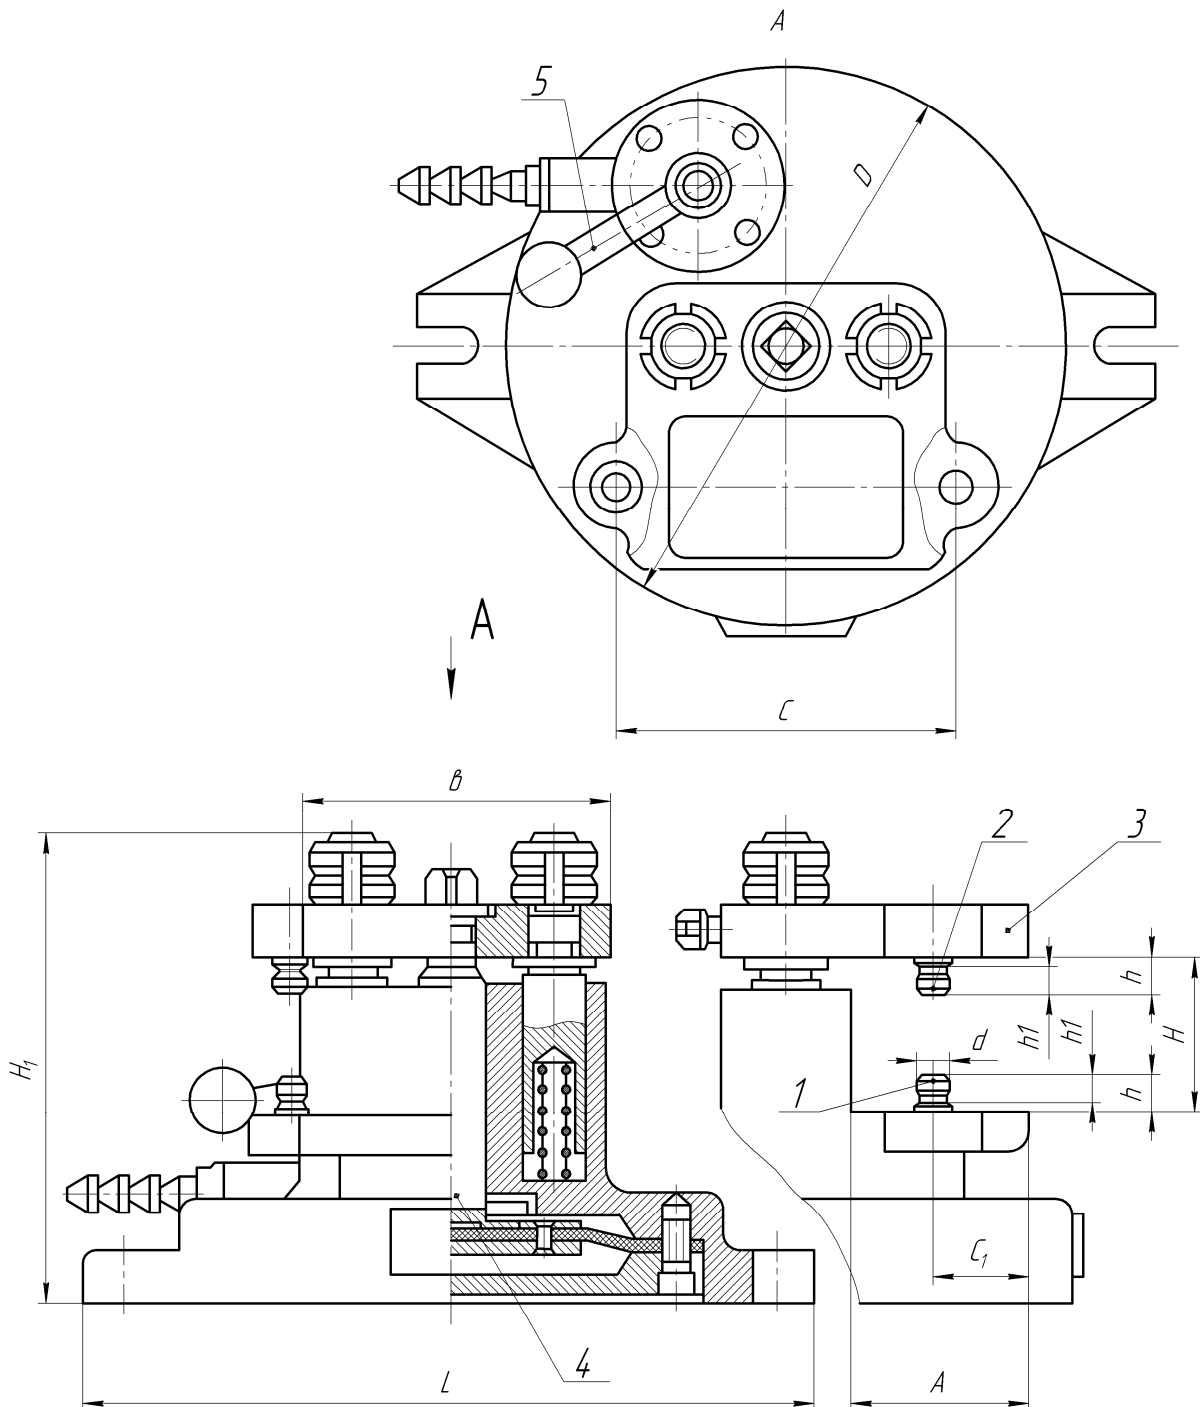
Будова й параметри кондуктора скальчастого двоколонного із пневматичним затискачем: 1, 2 – пальці; 3 – кришка; 4 – пневматичний привід; 5 – рукоятка
